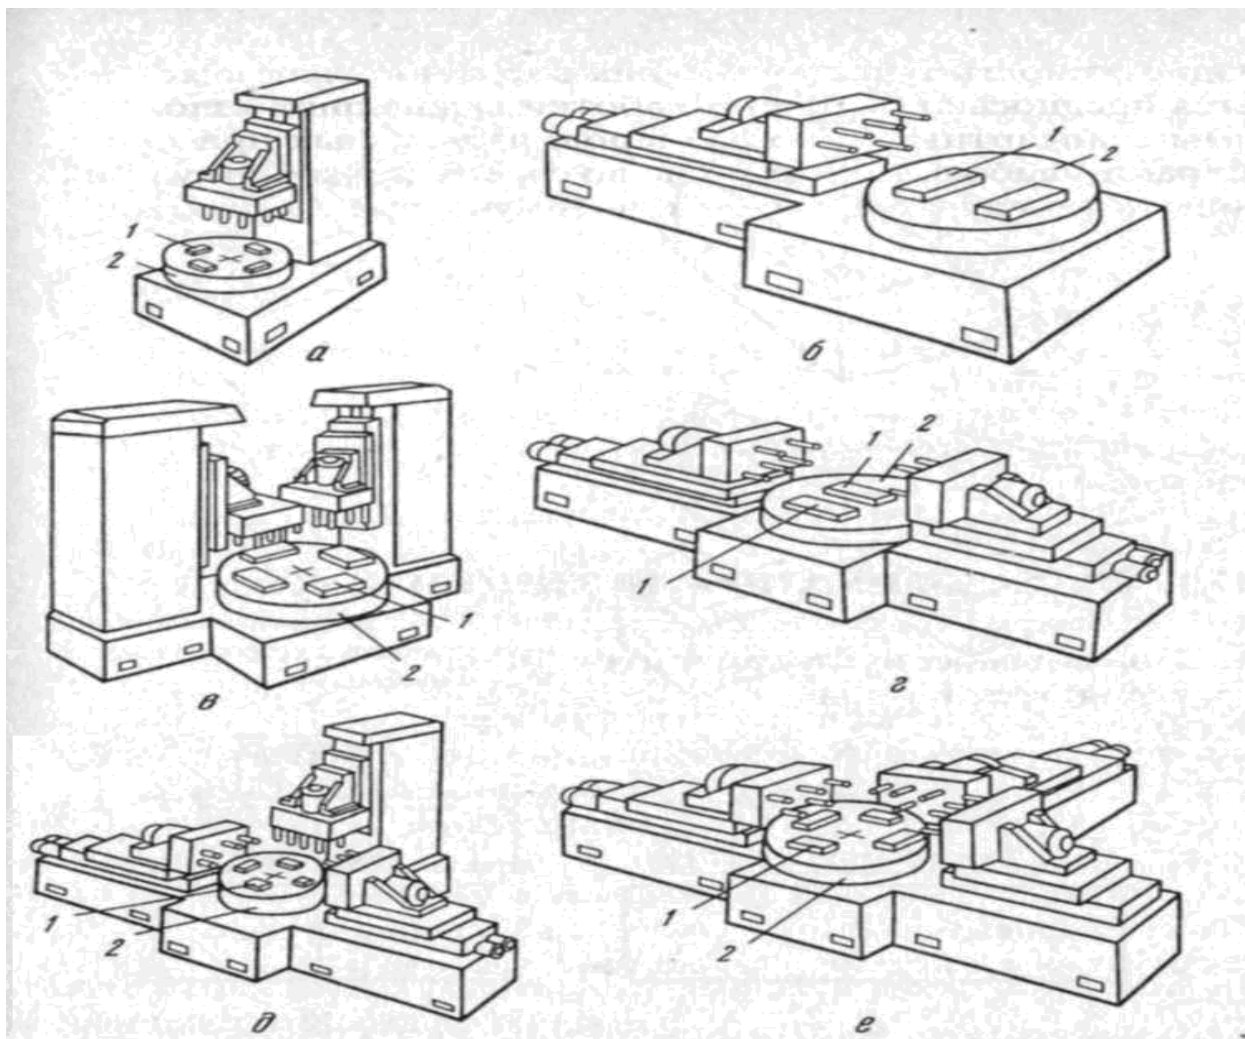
Типовые компоновки агрегатных станков с поворотным делительным столом.
